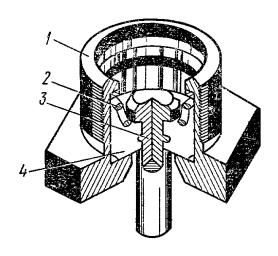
Вентиль спускной: 1 + корпус; 2 - пружина; 3 - шток; 4 - прокладка
